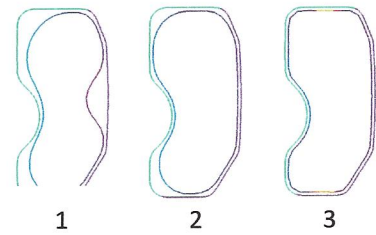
Querschnitt nach dem Schliessen des Werkzeugs (1), beim IHU-Prozess und ca. 300 bar (2) und ausgeformt (3).
